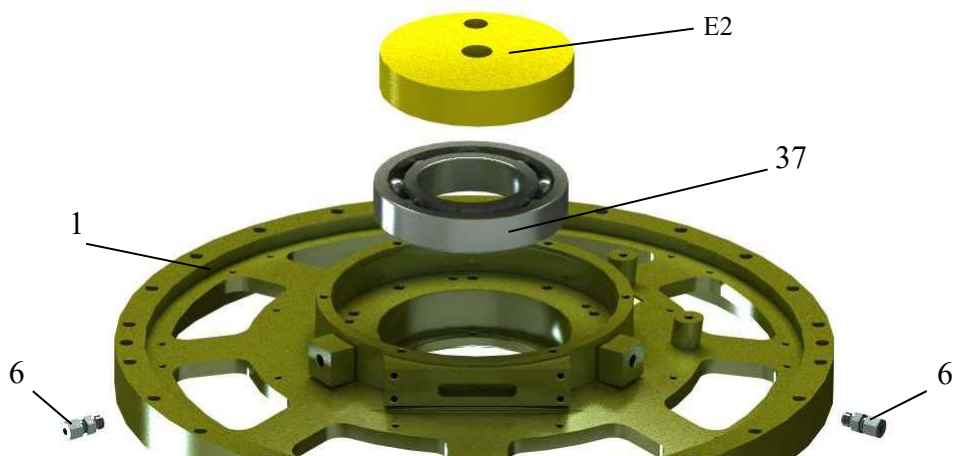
Установка шарикового подшипника в подшипниковый щит со стороны привода
